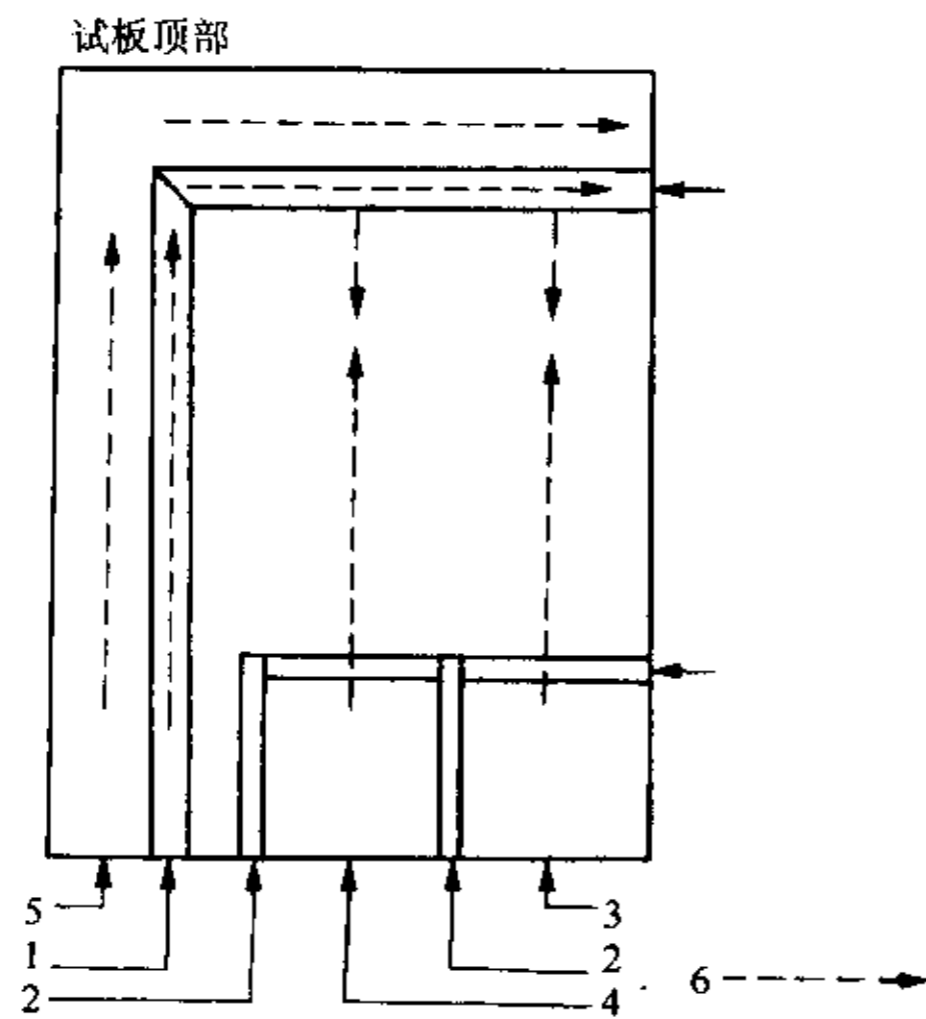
按 4.2.1.1、4.2.1.2、4.2.1.3 和 4.2.2.2 所制得的试板的布置和“找平”方向
